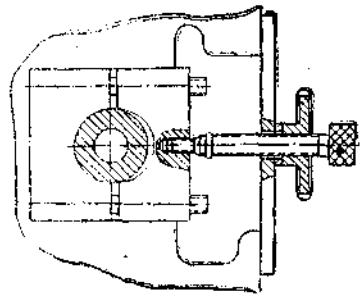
Приспособление для съема верхнего вкладыша подшипника распределительного вала
